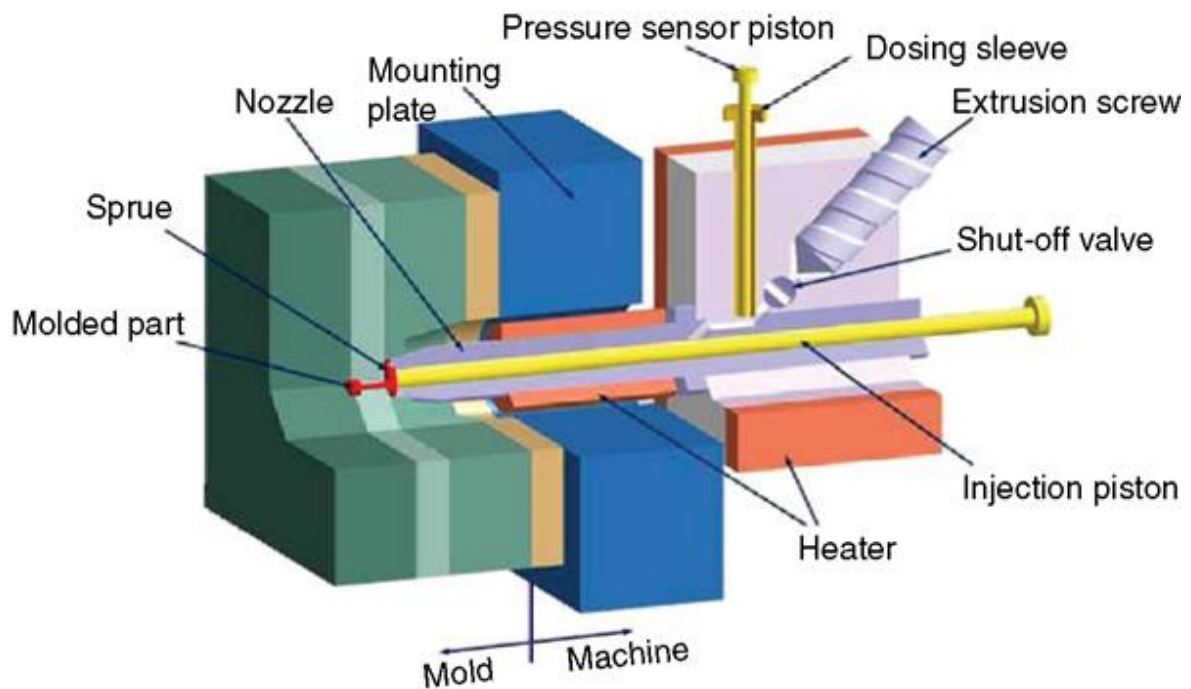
Unità di iniezione di una macchina per micro stampaggio
